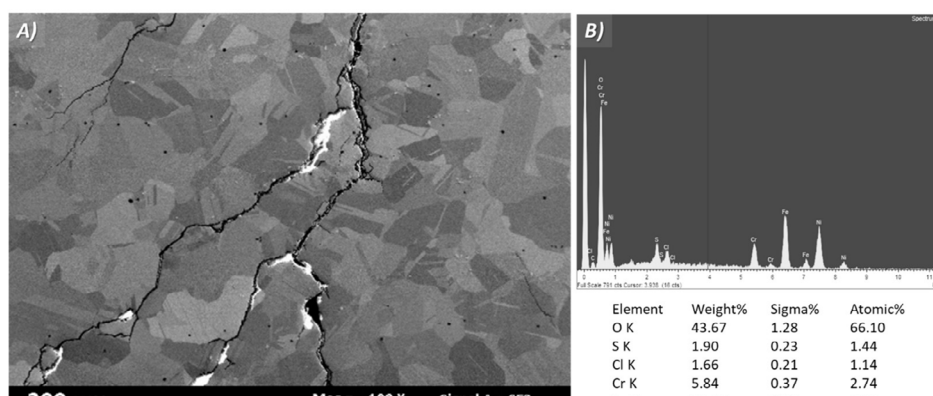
Cricca in sezione su paletta di turbina in lega 718 / Crack in section of turbine blade made of alloy 718.
